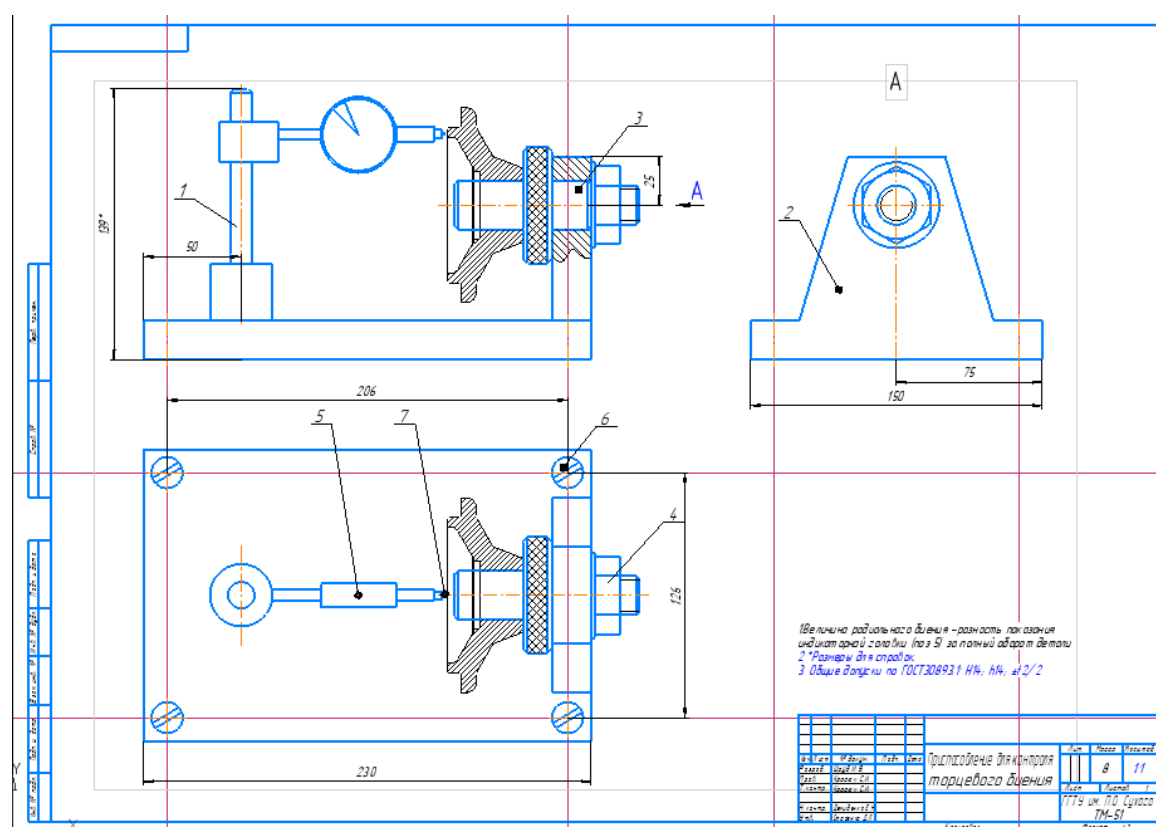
Чертеж приспособления для контроля торцевого биения
